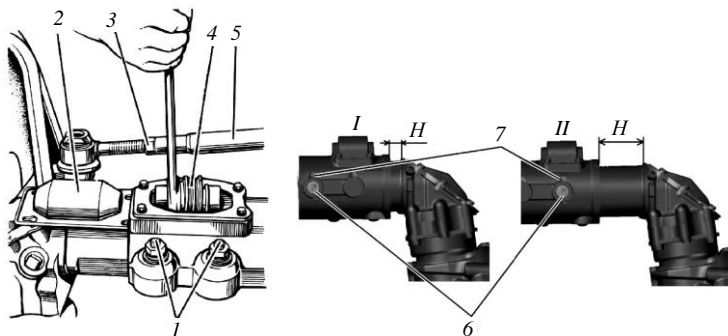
Схема изменения колеи передних колес трактора с коническими колесными редукторами: 1 – клинья; 2 – крышка регулировочного винта; 3 – гайка; 4 – регулировочный винт; 5 – труба рулевой тяги; 6 – фиксирующий палец; 7 – шплинт
